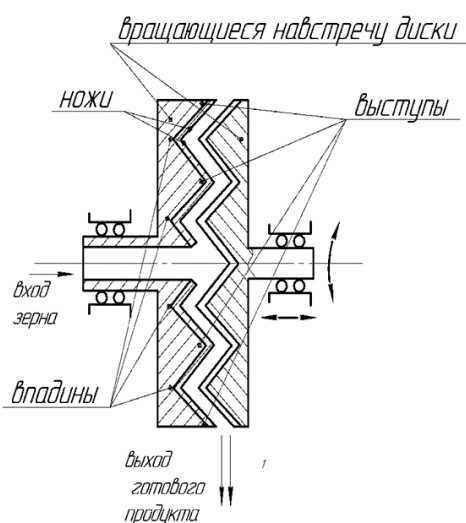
Схема двухдискового ударно-центробежной зернодробилки
